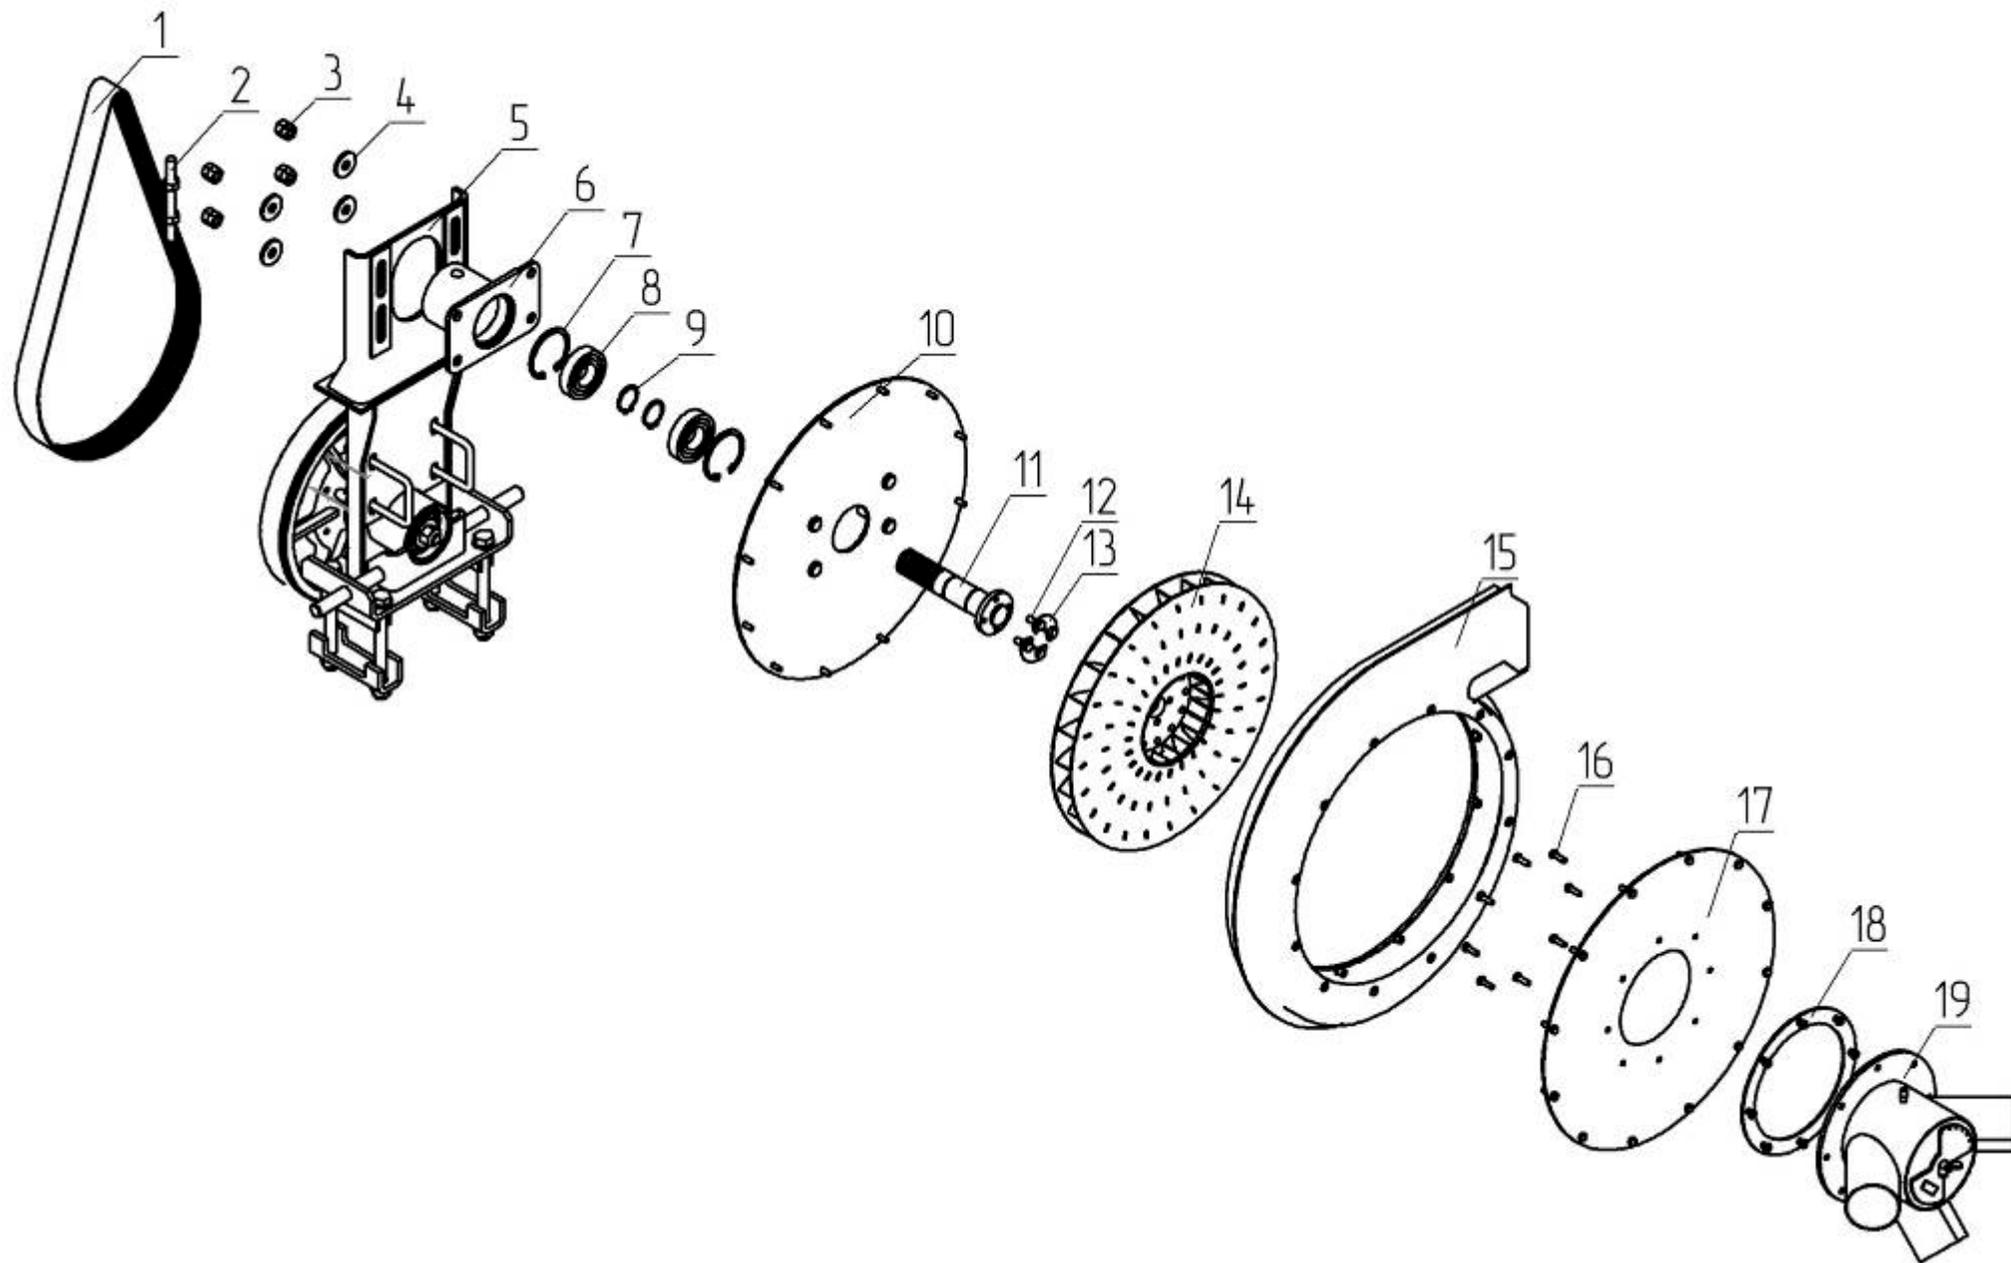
Вентилятор 509.046.7710. Верхний вал
